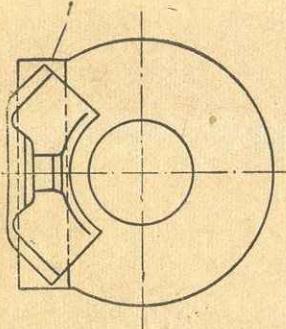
Расположение щупа при регулировке ручного тормоза:
